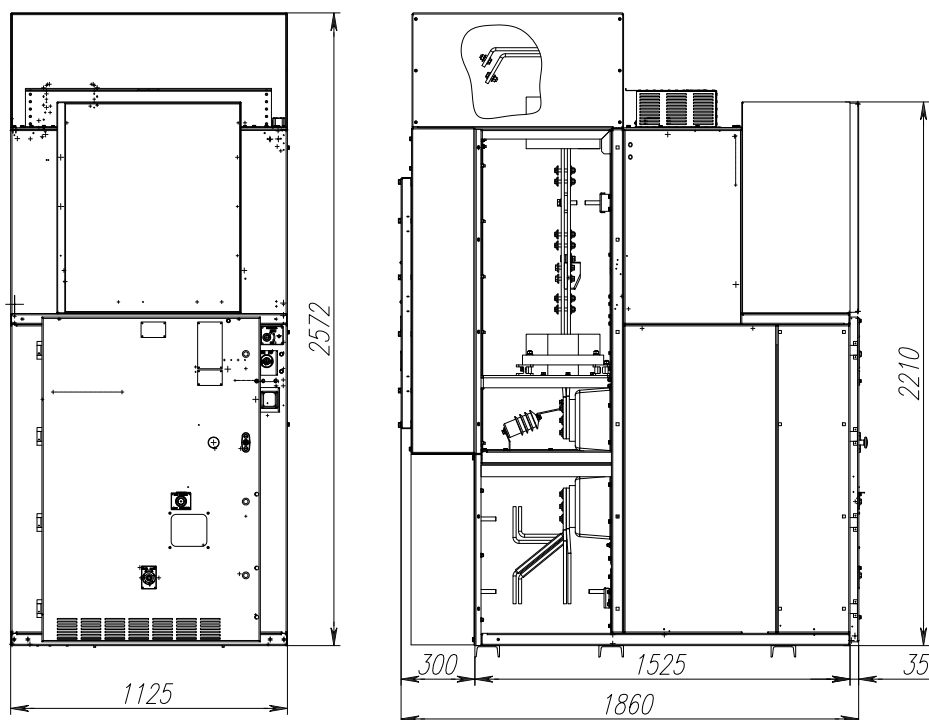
Общий вид и габаритные размеры шкафа К-128 шинного ввода с двумя группами ТТ на номинальные токи 2000-4000 А
